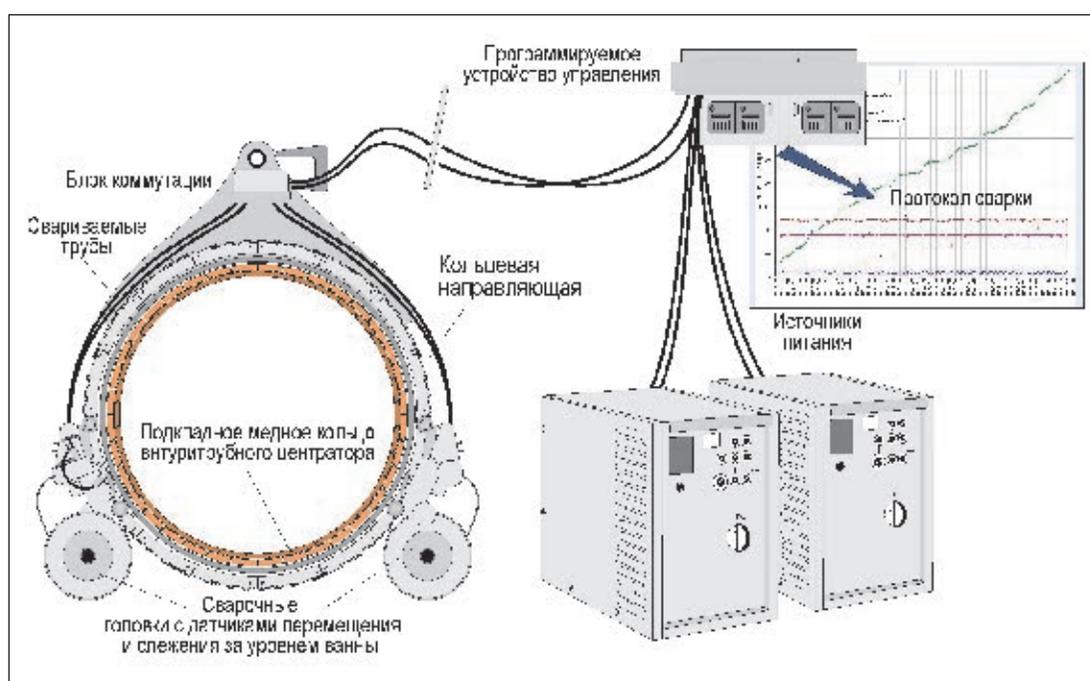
Схема комплекса основного оборудования для дуговой сварки порошковой проволокой неповоротных стыков труб
